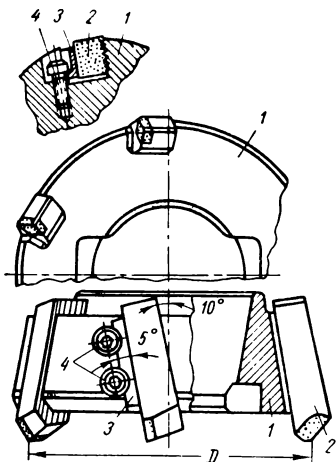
Крепление клином и винтами плоских ножей с рифлями в корпусе торцевой фрезы:
